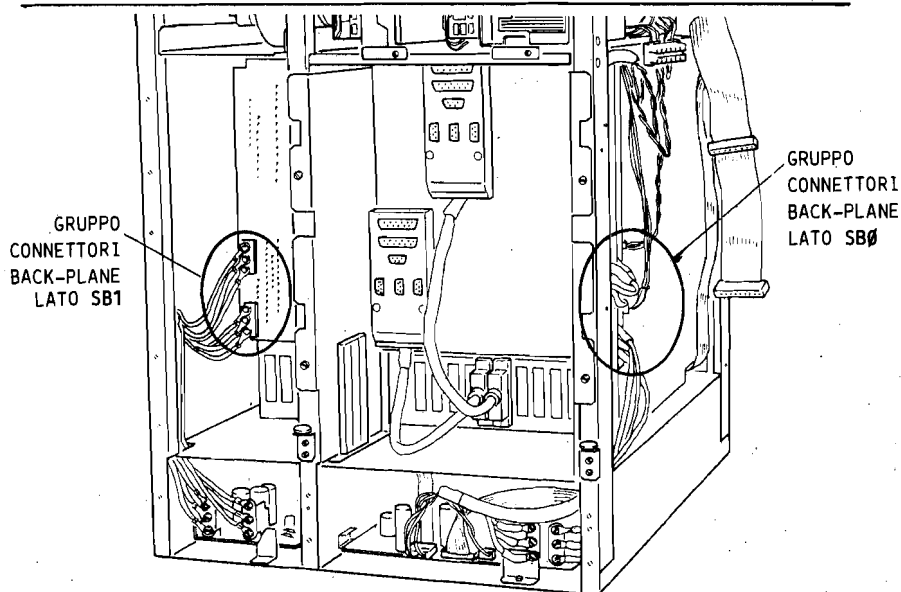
Posizione dei connettori del BACK PLANE riferita alla struttura del sistema
